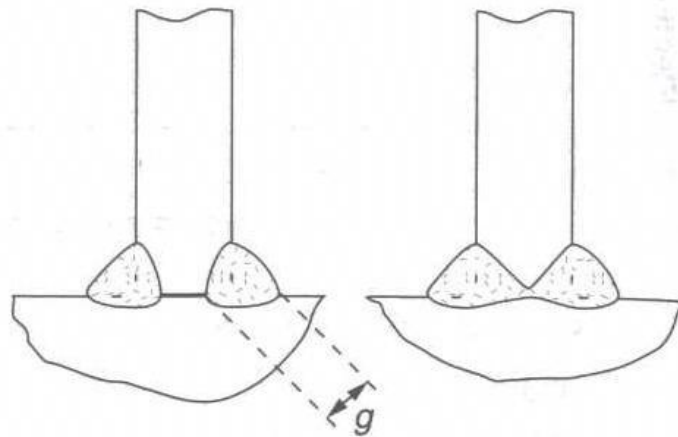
Comment améliorer la limite d'endurance d'un assemblage soudé.
